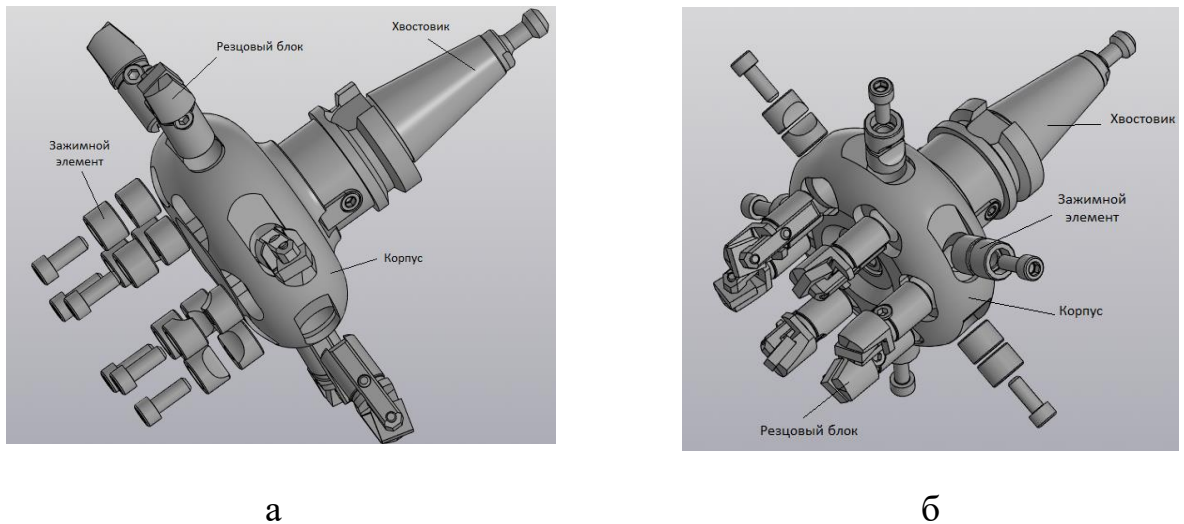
Внешний вид комбинированной фрезы: а – дисковой; б – торцовой
